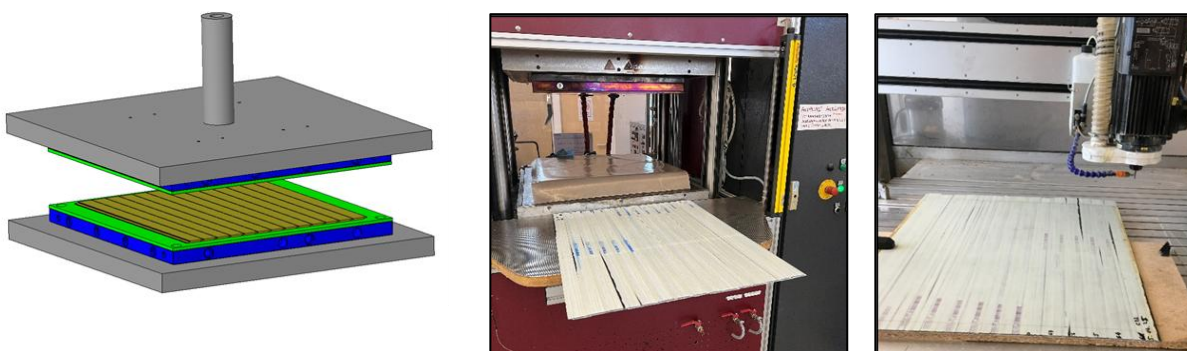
links: Werkzeugkonzept im CAD; Mitte: Manuelles Einlegen der Pultrusionsprofile ins Werkzeug zum Verpressen; rechts: Zu einer Platte verpresste Pultrudate bei der Besäumung in der Fräse
